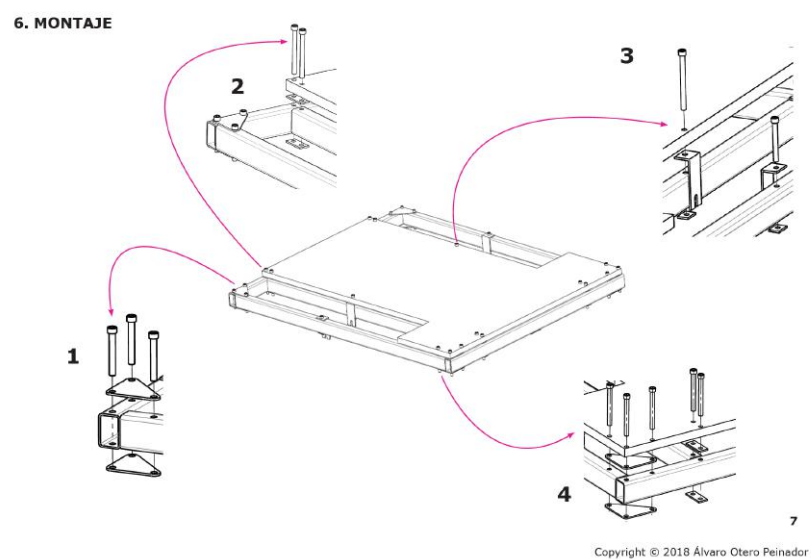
Ejemplo del manual de ensamblaje: Ensamblaje - Creado con InDesign por Álvaro Otero.
